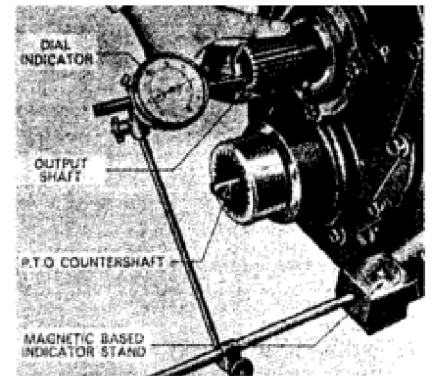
Controle transmissie output shaft einde spelen met wijzerplaat indicator.
